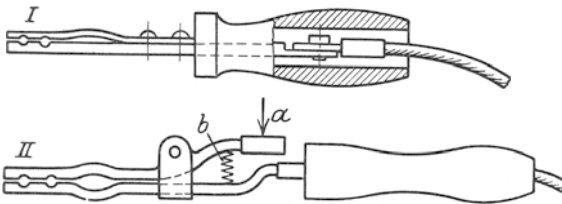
Schweißzange für Kaltschweißungen.
